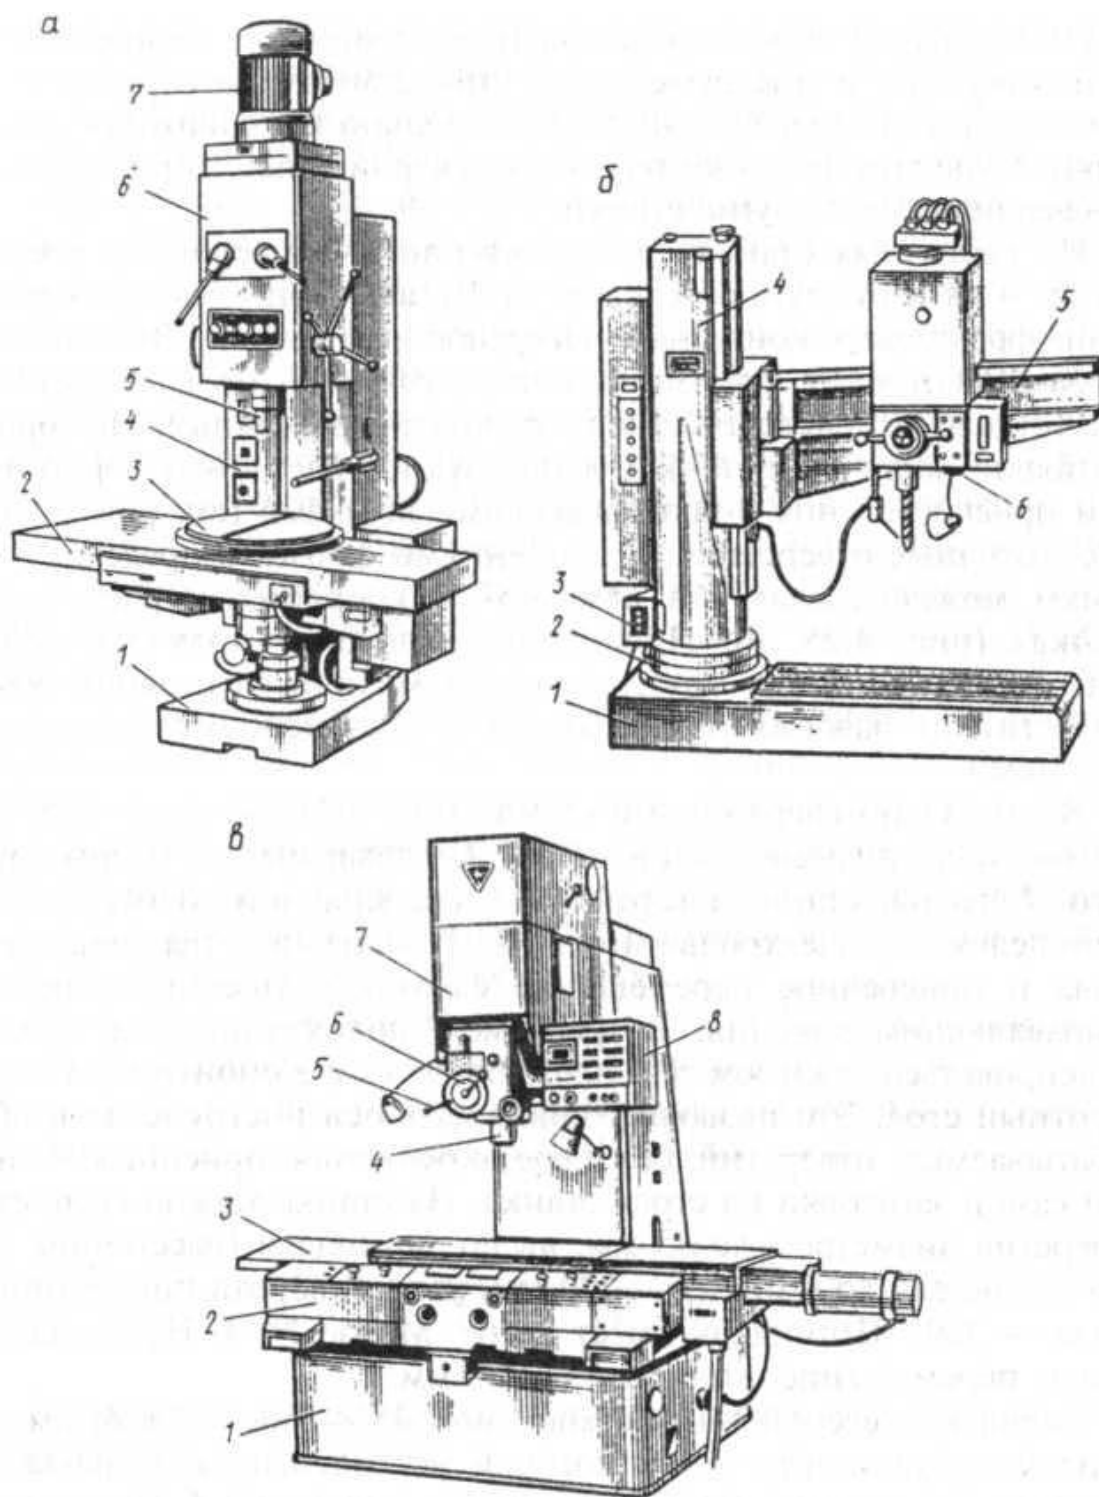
Общий вид станков сверлильно-расточной группы: а – вертикально-сверлильный мод. 2Н135-1; б – радиально-сверлильный мод. 2554; в – координатно-расточной мод. 2А450Ф30
